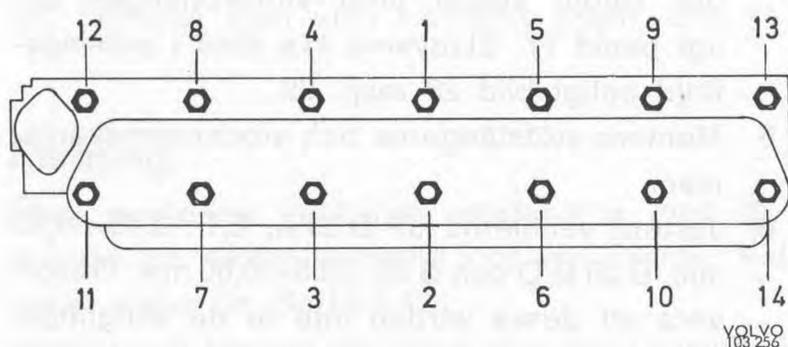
Åtdragningsföljd för cylinderlocksskruvar, B 30
